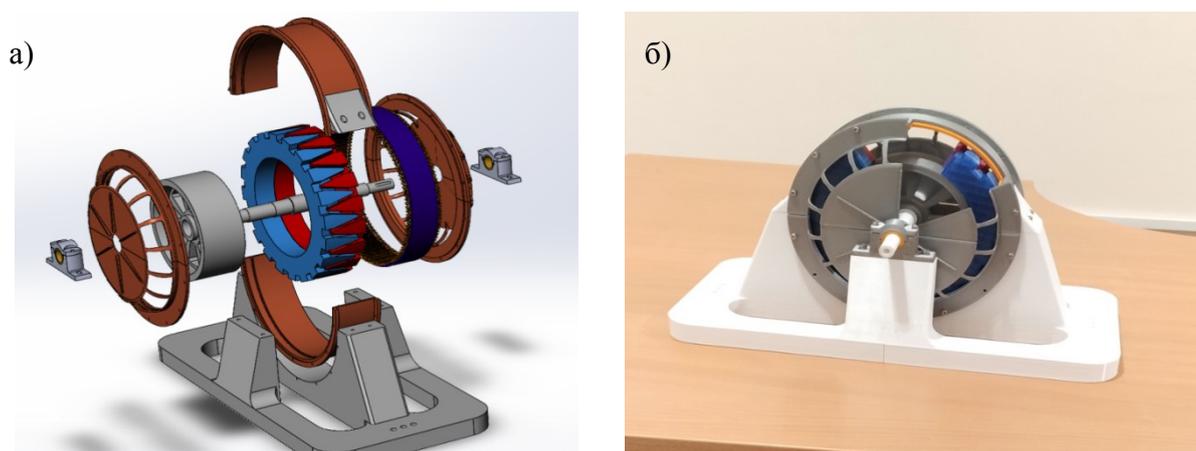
Трехмерная твердотельная модель и масштабный макет ВДКП
